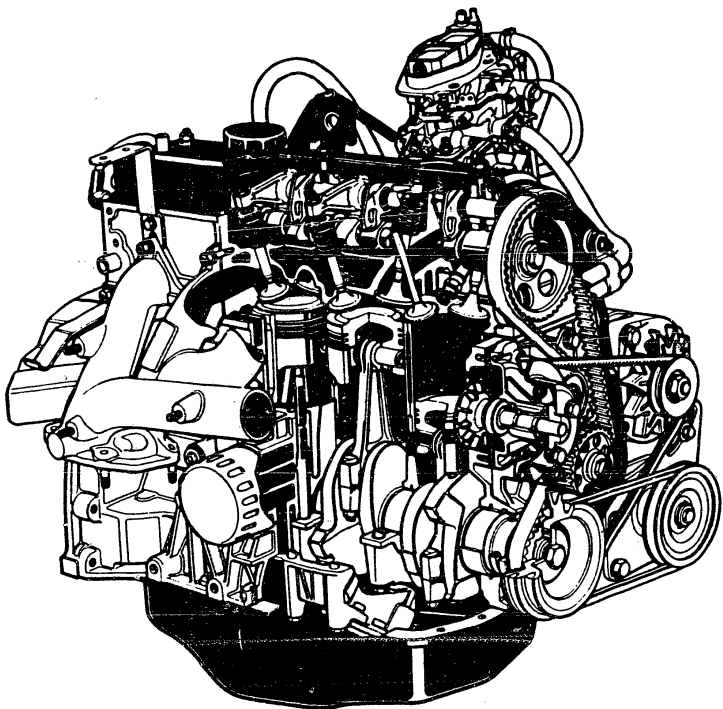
Der Benzinmotor J6R mit Leichtmetall-Zylinderblock und nassen Zylinderlaufbüchsen. Es bedeuten:
